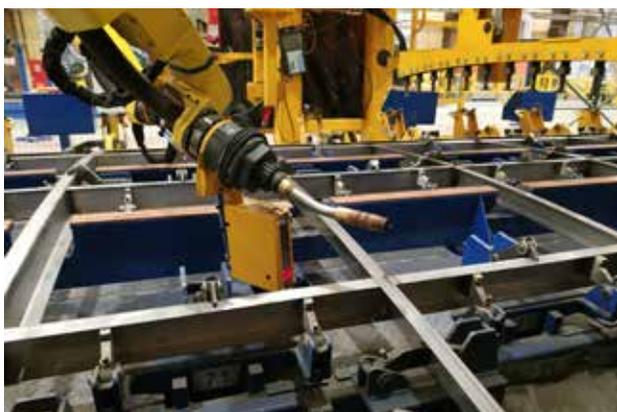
Общий вид роботизированного комплекса для сварки крыши вагонов метро:
